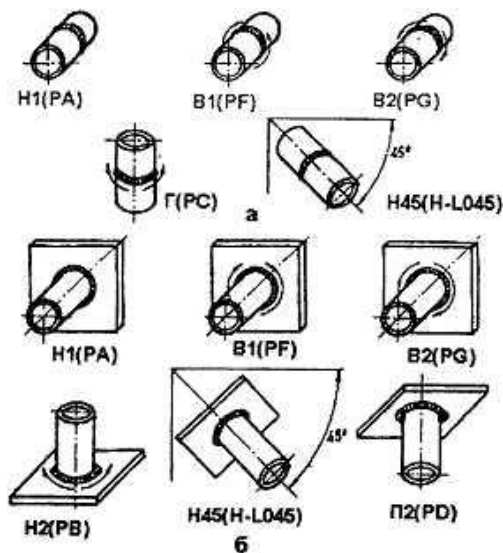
Положение шва при сварке стыковых (а) и угловых (б) соединений труб:
